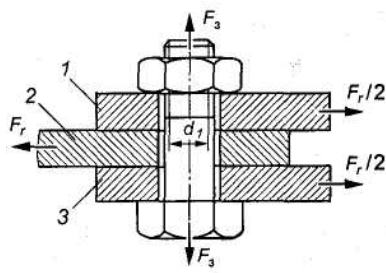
К расчёту болтового соединения, несущего поперечную нагрузку. Болт установлен с зазором
